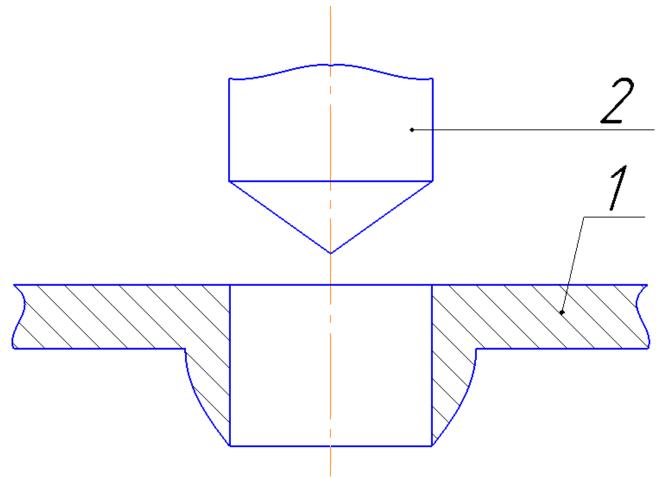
Увеличениедлинырезьбового отверстия за счётобразования отбортовки[2]: 1 — заготовка; 2 — пуансон
